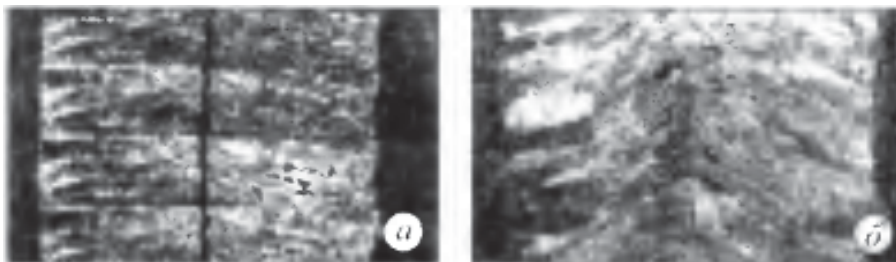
Расположение трещин по сечению шва при электрошлаковой сварке:
